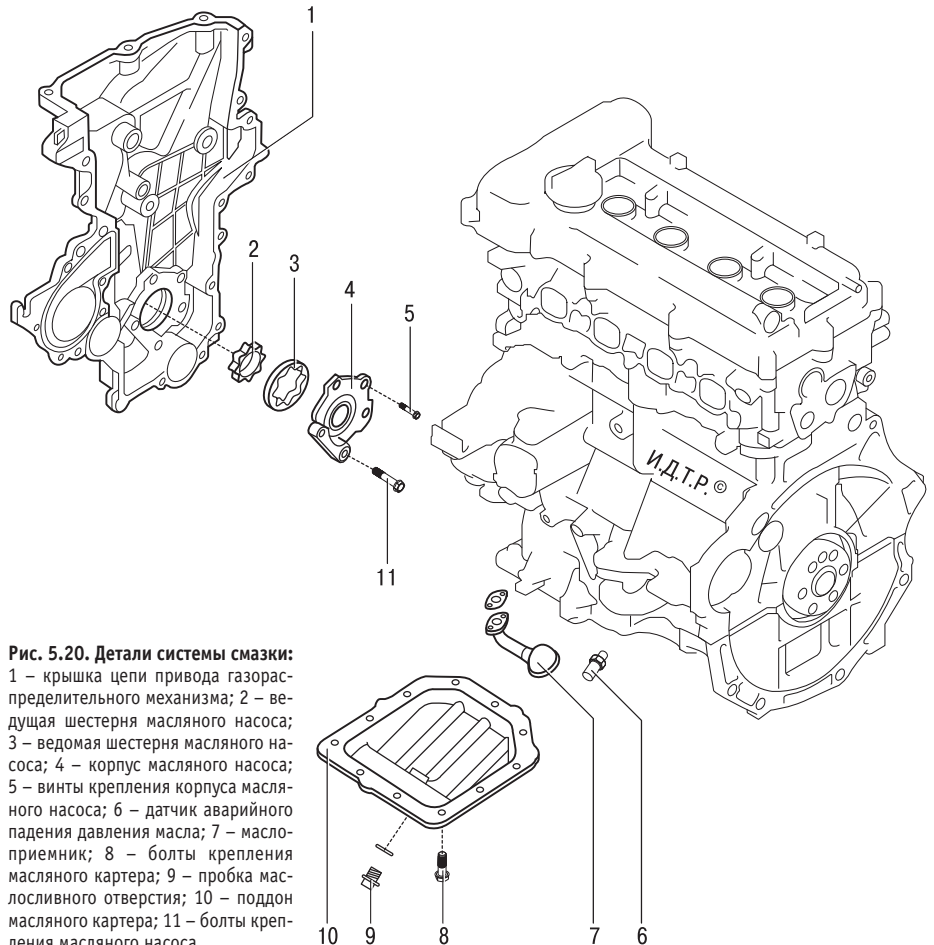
Детали системы смазки: 1 – крышка цепи привода газораспределительного механизма; 2 – ведущая шестерня масляного насоса; 3 – ведомая шестерня масляного насоса; 4 – корпус масляного насоса; 5 – винты крепления корпуса масляного насоса; 6 – датчик аварийного падения давления масла; 7 – маслоприемник; 8 – болты крепления масляного картера; 9 – пробка маслосливного отверстия; 10 – поддон масляного картера; 11 – болты крепления масляного насоса
